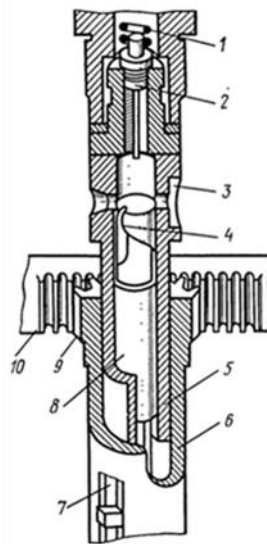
ТНВД золотникового типа: 1 - пружина; 2 - нагнетательный клапан; 3 - топливная рейка; 4 - управляющий поясок; 5 - втулка плунжера; 6 - поворотная втулка; 7 - прорези; 8 - плунжер; 9 - зубчатый венец; 10 - зубчатая рейка.
